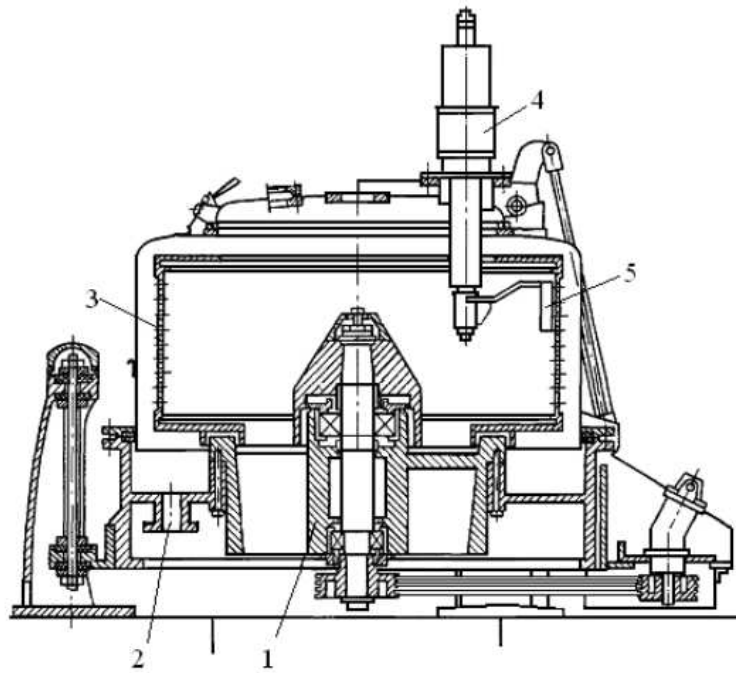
Центрифуга типу ФМН: 1 — корпус приводу; 2 — штуцер; 3 — ротор; 4 — механізм зрізання осаду; 5 — ніж
